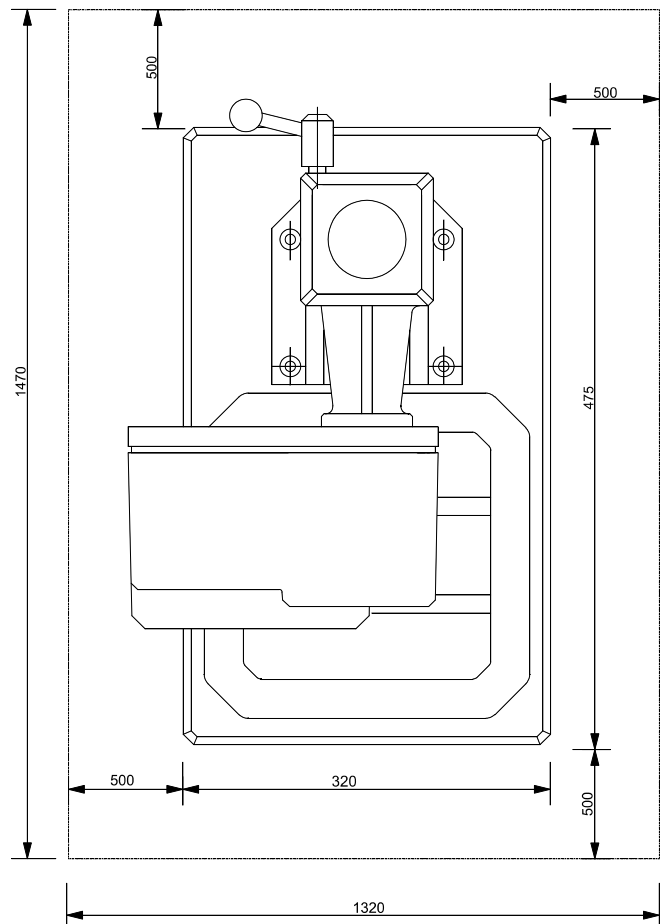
Aufstellplan, Flächenbedarf der Maschine (Maße in mm)
